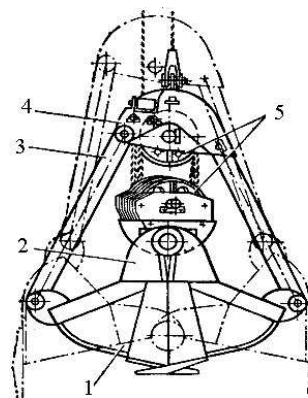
Типовой грейфер двухканатный длиннозвеньевой симметричный
